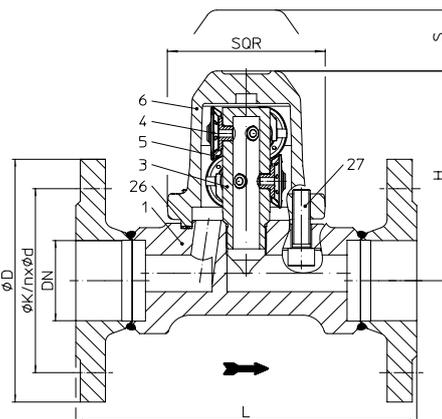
1....6K2 (DN40-50) com 6 cápsulas, com flanges
